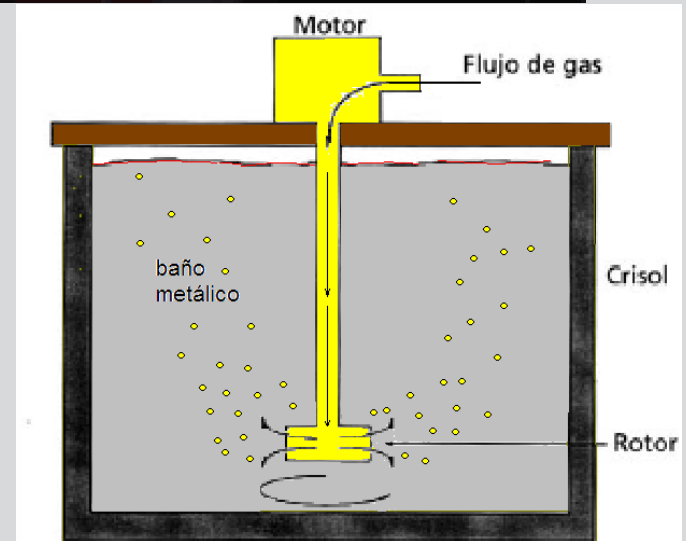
Olla (cuchara) equipada con rotor inyector.
